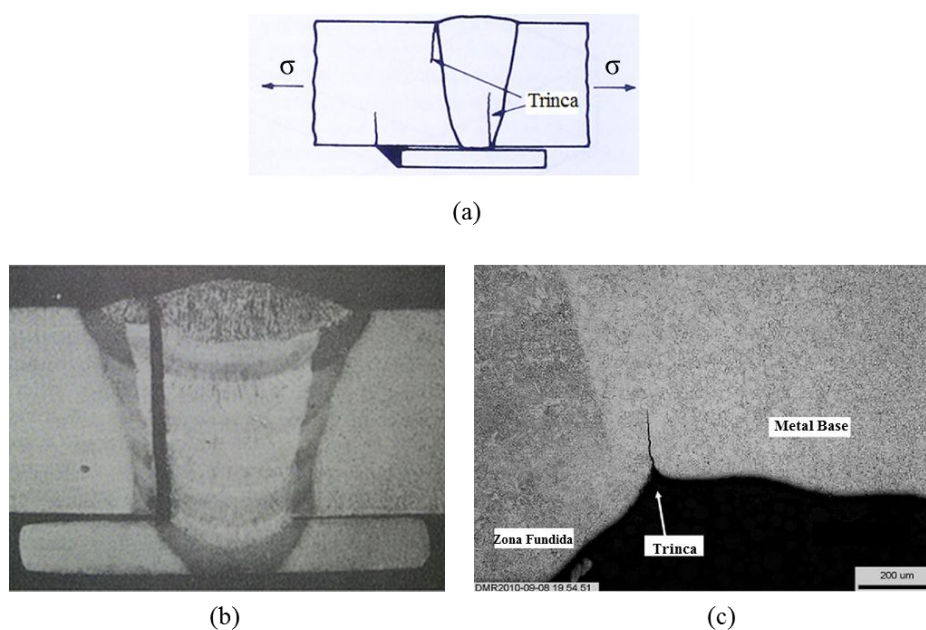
(a) Representação esquemática dos principais pontos de iniciação de trinca numa junta soldada multipasses; (b) Macro secções com trincas por fadiga em junta de topo com *backing* metálico, adaptação de BRANCO *et al.*, (1999); c) Trincamento na ZTA na solda de um tubo, adaptação de ZHANG e MADDOX (2012).
